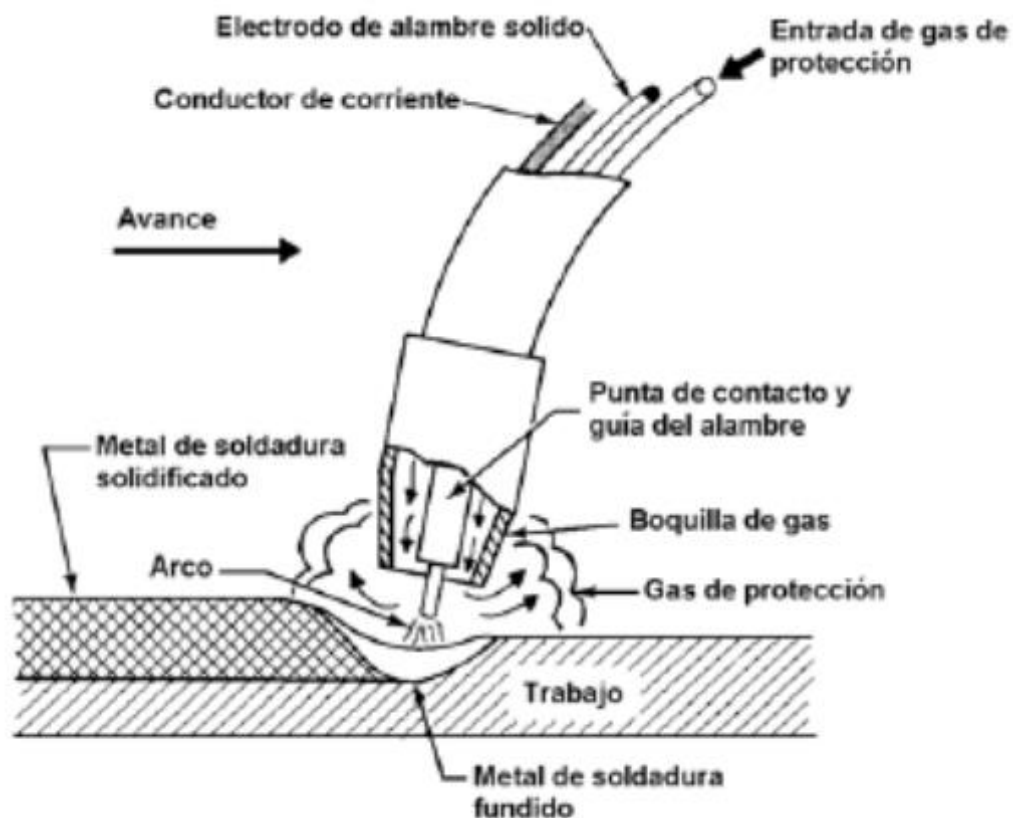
Soldadura por arco metálico en atmosfera gaseosa (GMAW)
